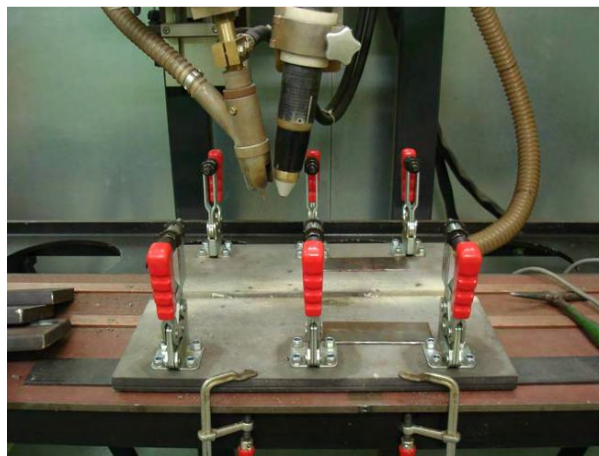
Probeneinspannung für die Schweißversuche
